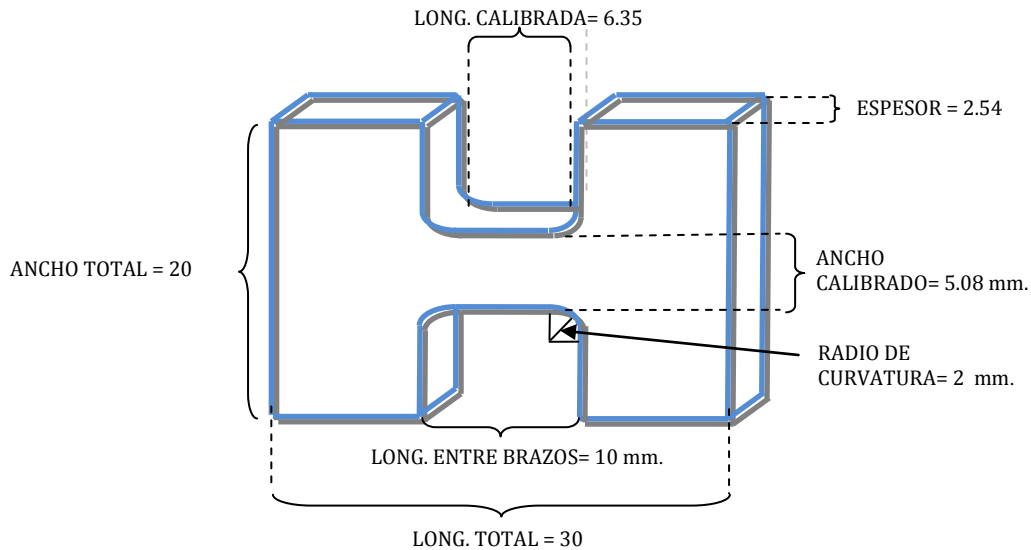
Esquema y dimensiones de la probeta maquinada.
